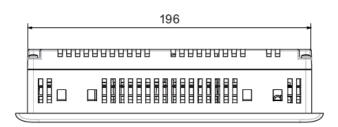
Dimensiones técnicas del Panel TP177B PN/DP
